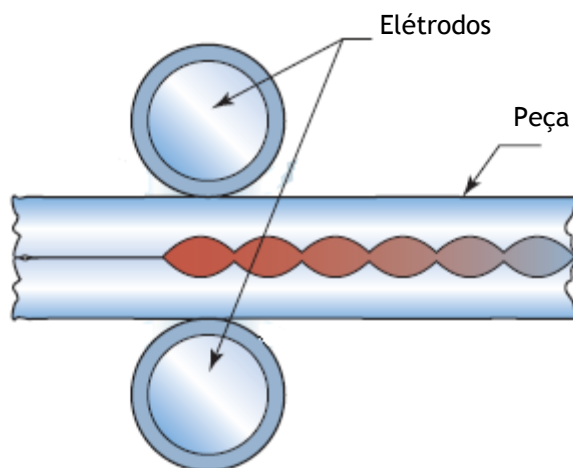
Princípio da soldadura por resistência do tipo costura
